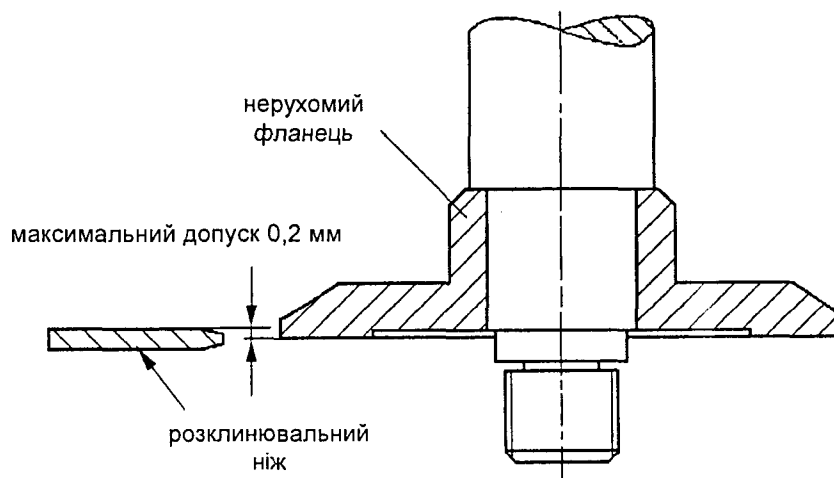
Положення розклинювального ножа щодо нерухомого фланця
